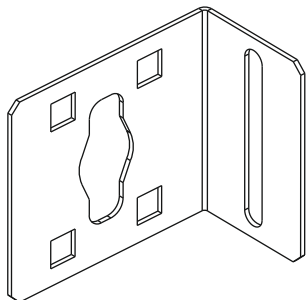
Внешний вид кронштейна углового блока розеток / Figure 2 – Appearance of the angle power strip bracket /
